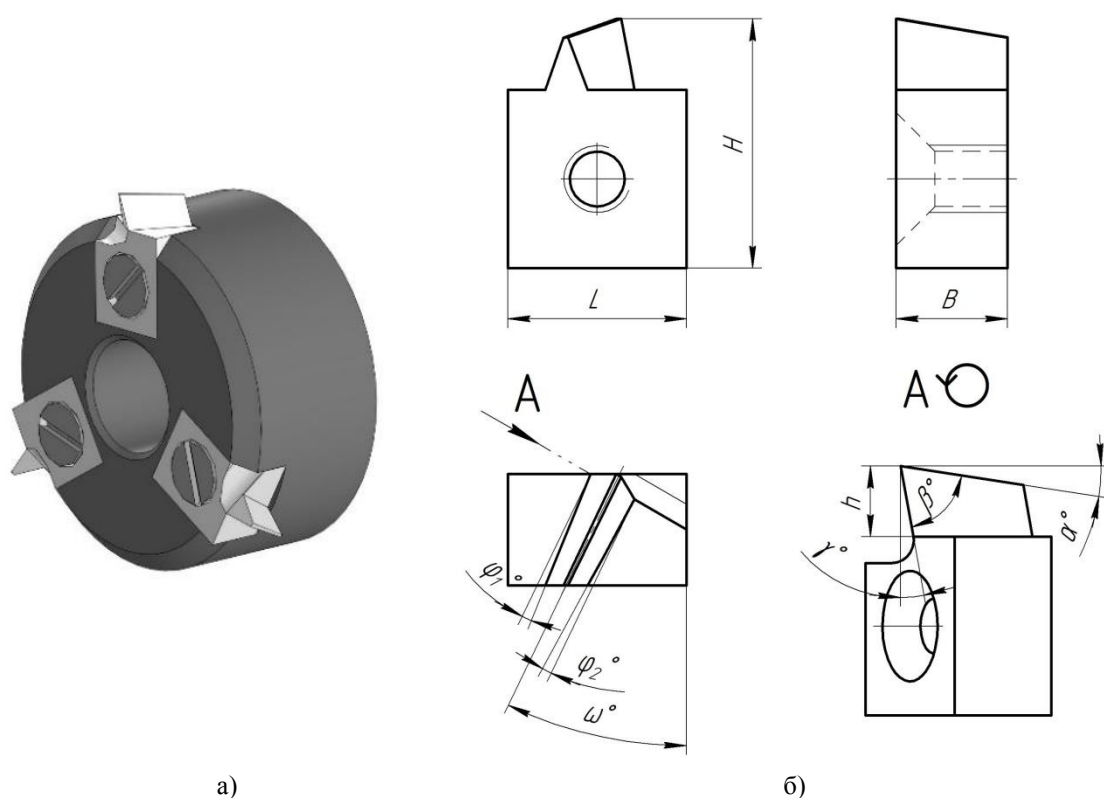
Сектор режущего инструмента для обработки внутренних винтовых канавок: а - трехмерная модель режущей оправки; б - геометрические характеристики режущей пластины: γ - передний угол; α - задний угол; β - угол заострения; ω - угол наклона режущего зуба; ϕ_1 , ϕ_2 - вспомогательные углы в плане; h - высота режущего зуба; H , L , B - габаритные размеры режущей пластины
